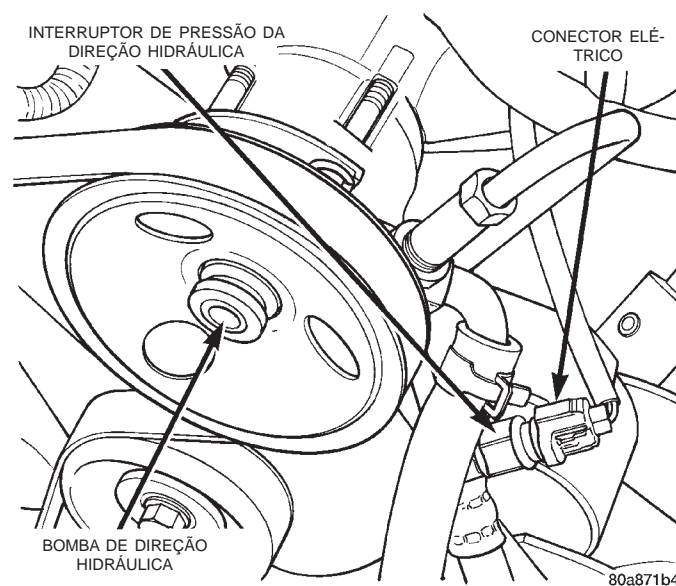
Interruptor de Pressão da Direção Hidráulica
